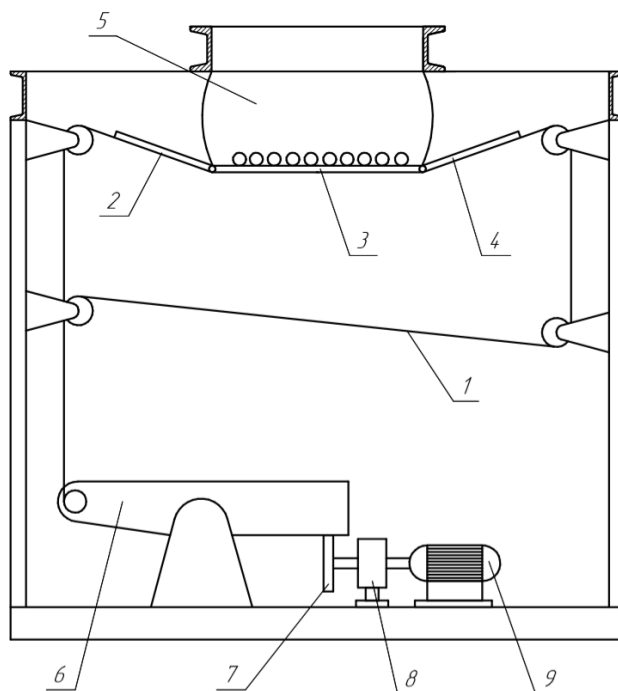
Принципиальная схема устройства для вибрационной ударно-импульсной обработки деталей: 1 – гибкая нить; 2, 3, 4 – жесткие площадки; 5 – рабочая камера; 6 – кулиса; 7 – кулачок; 8 – редуктор; 9 – двигатель
